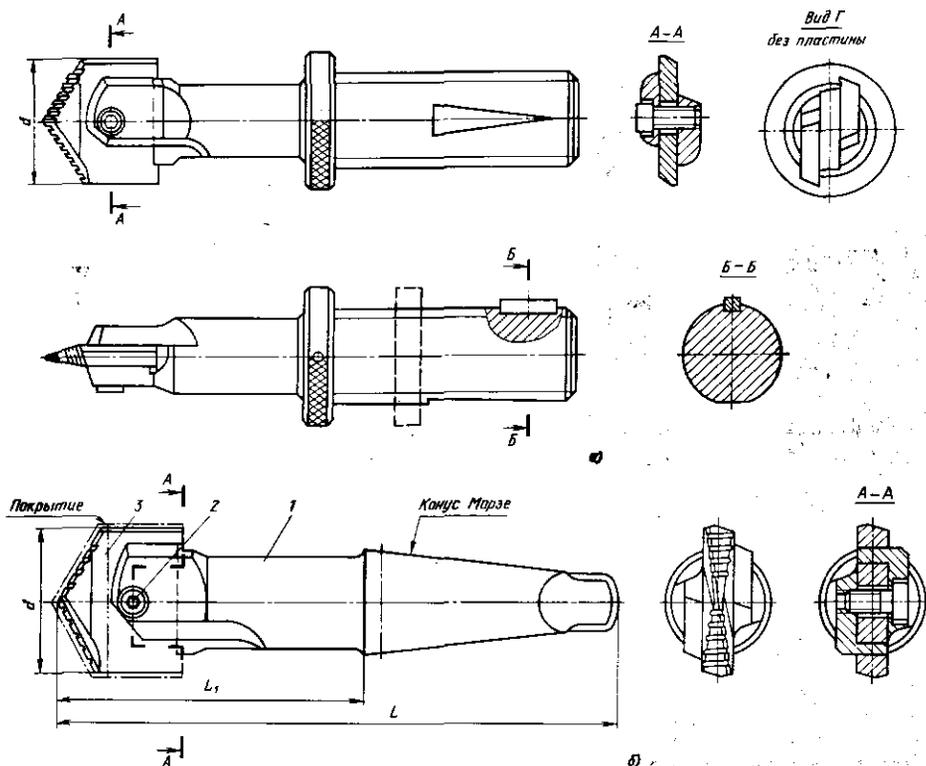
Сборные первые сверла: 1 — державка; 2 — фиксирующий винт; 3 — пластина
